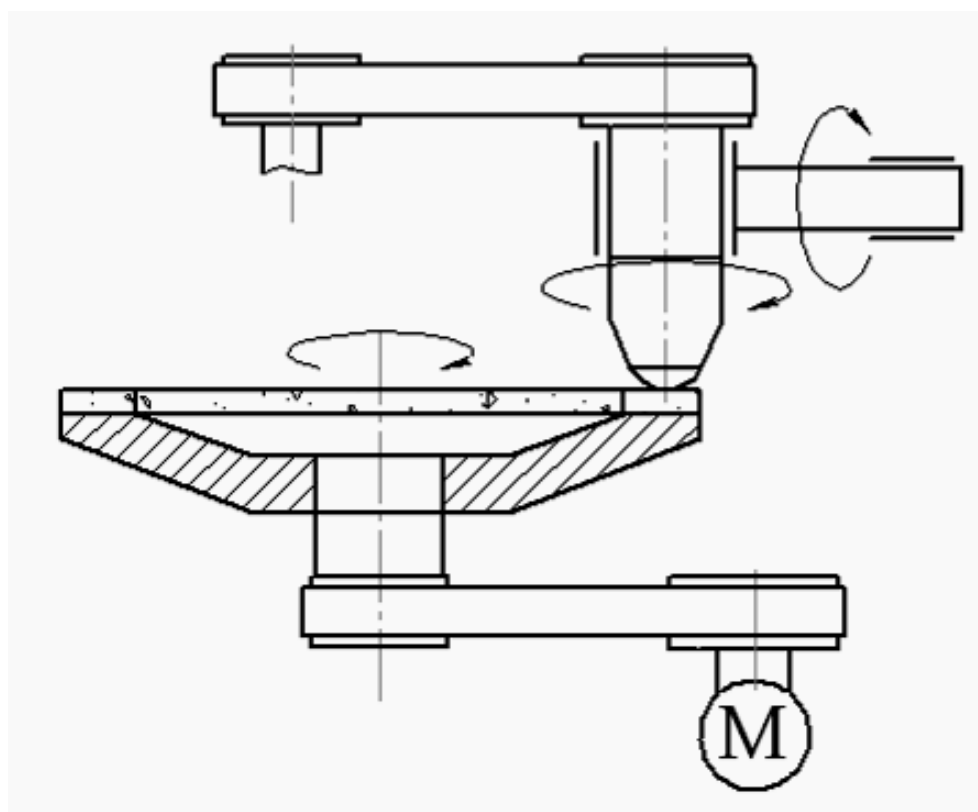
Кинематическая схема установки для заточки выглаживателей
